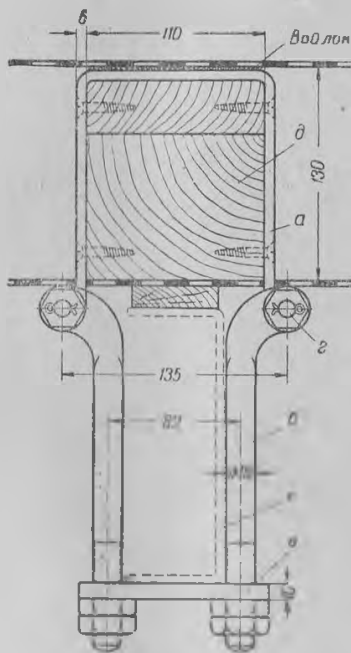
Конструкция крепления кузова авторефрижератора АР-5 к шасси:
